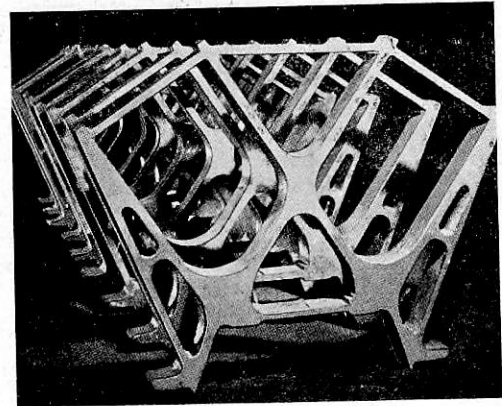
Geschweißter Kurbelkasten des 660 PS-Achtzylinder-Reihenmotors.
